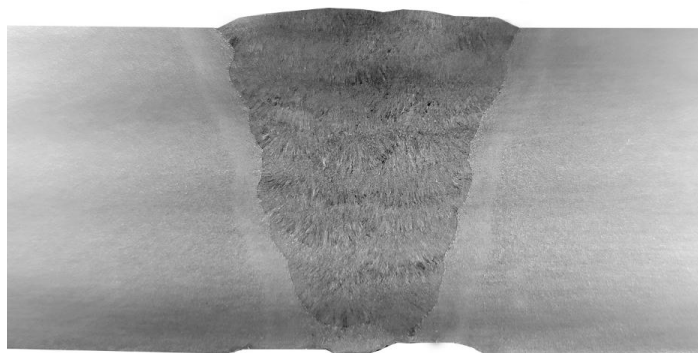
Макроструктура контрольного сварного соединения
